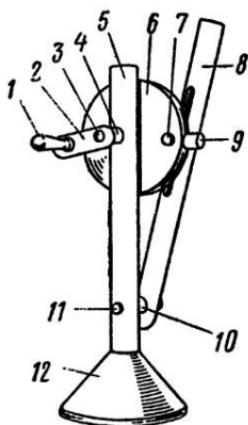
Элементарная модель кулисного механизма: 1 — ручка; 2 — рычаг ручки; 3 — вал привода; 4 — упорное кольцо; 5 — стойка; 6 — маховое колесо; 7 — «камень» кулисы; 8 — кулиса; 9 — стопорный винт; 10 — упорное кольцо; 11 — ось; 12 — основание.
